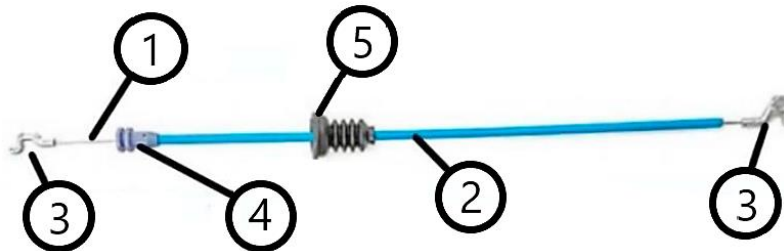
Exemplo de conjunto Bowden Cable – Adaptado de [52]
